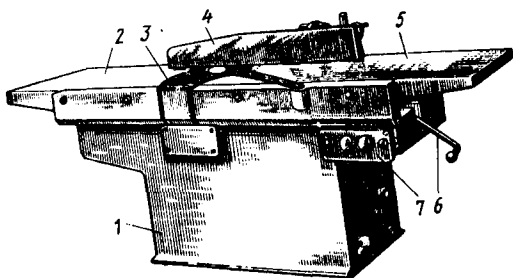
Фуговальный станок с ручной подачей СФ4-1:
